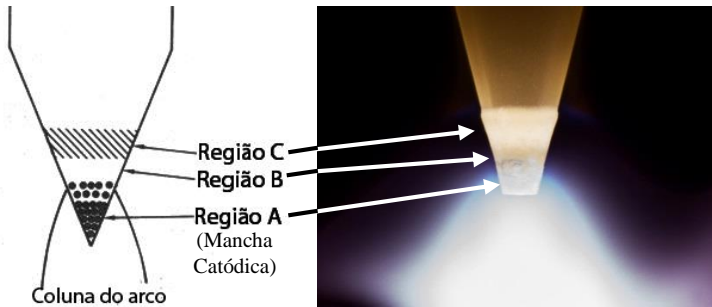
Regiões que compõem um arco de soldagem no processo TIG.
